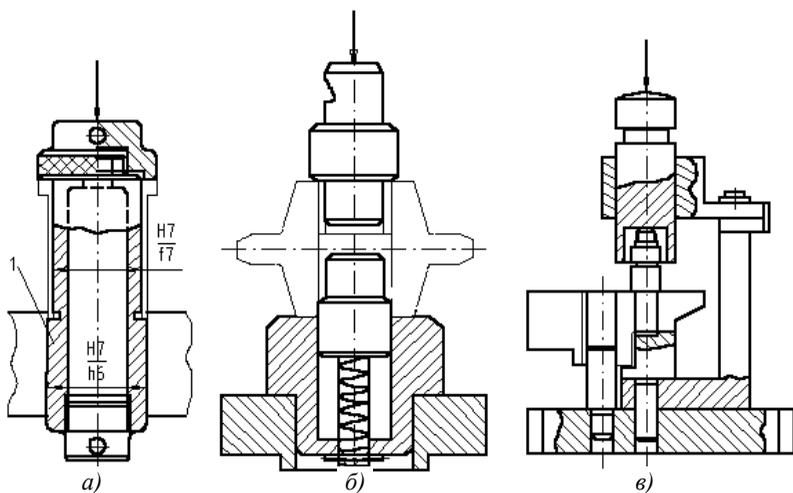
Приспособления, обеспечивающие направление деталям при запрессовке и выпрессовке
